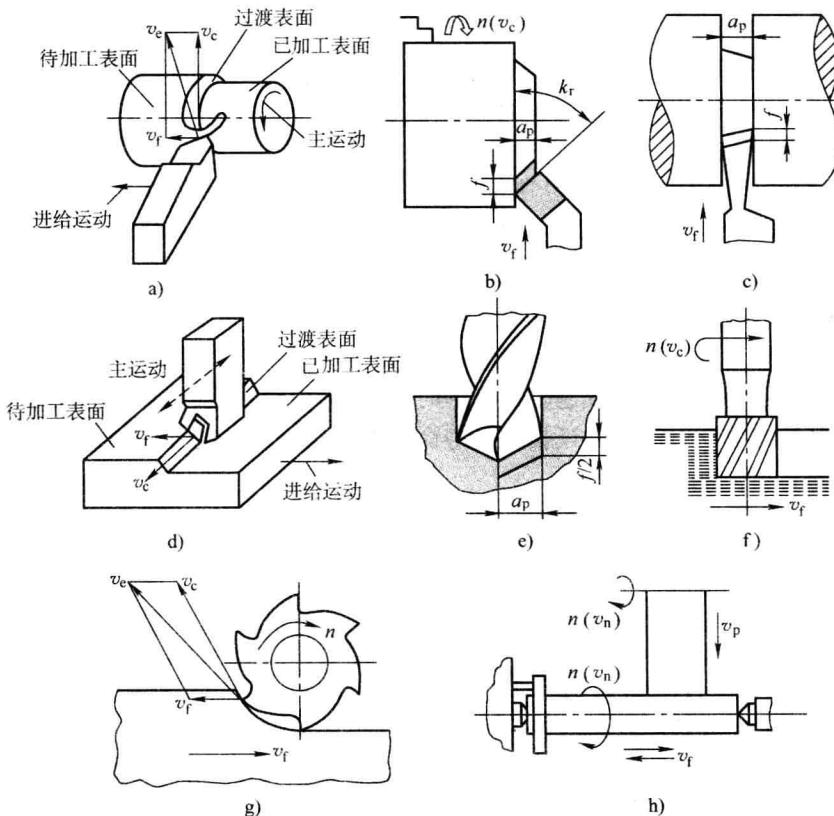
常见加工方法的加工表面、切削运动及切削用量
